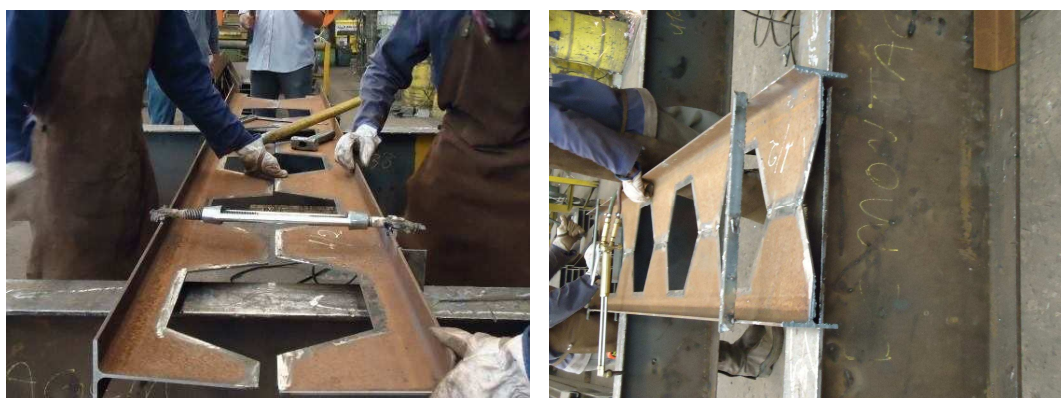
Finalização do posicionamento das metades e pré-montagem da viga castelada.
